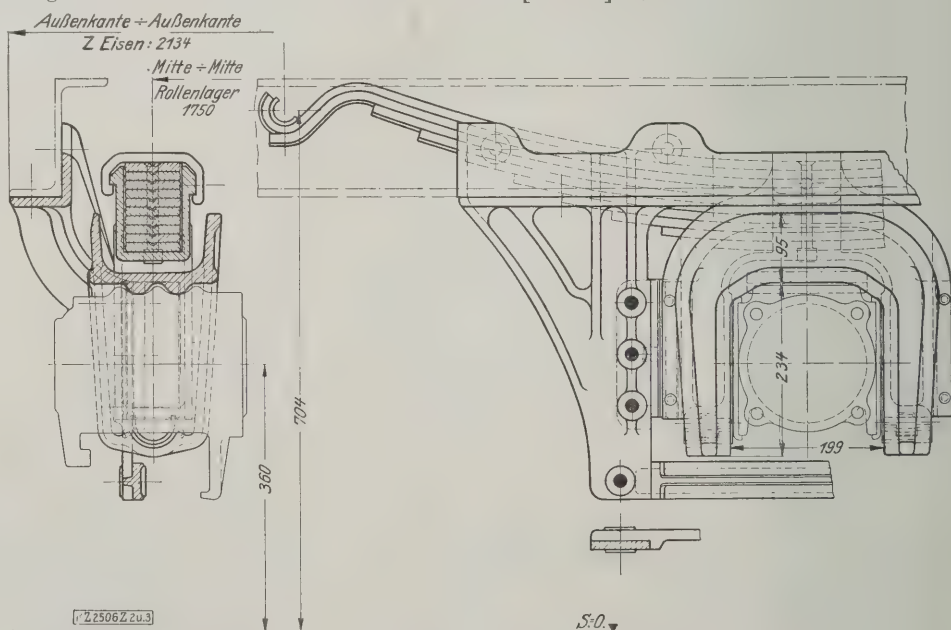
und 3. Peckham-Aufhängung mit oben liegender Feder
